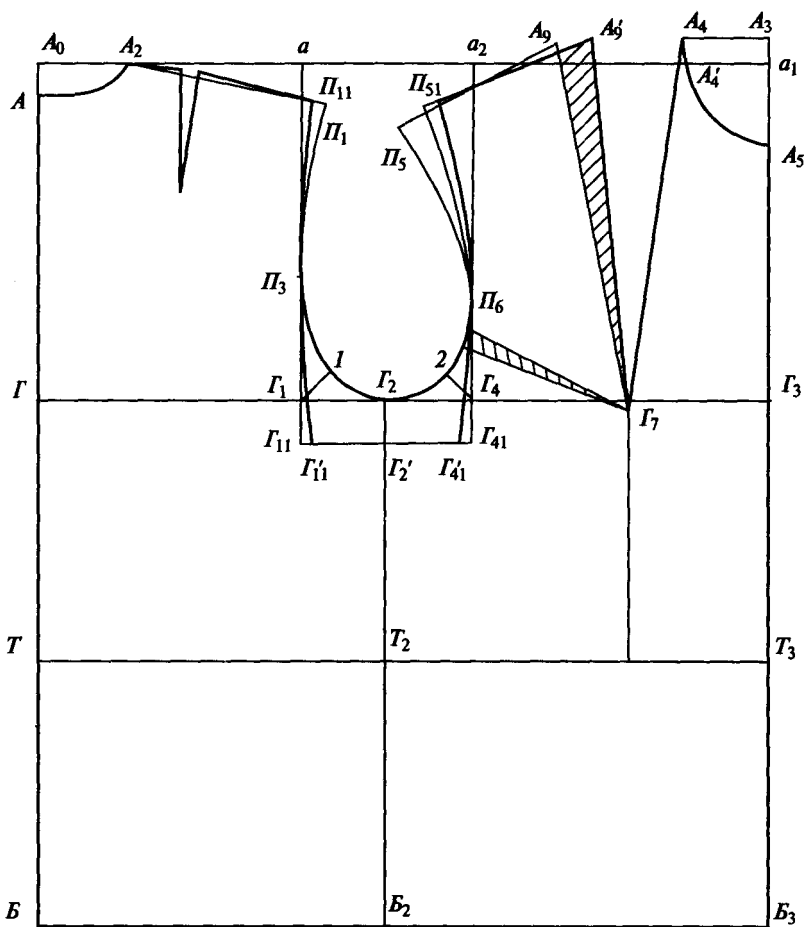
Чертеж конструкции изделия с рукавами рубашечного покрова с квадратной проймой
